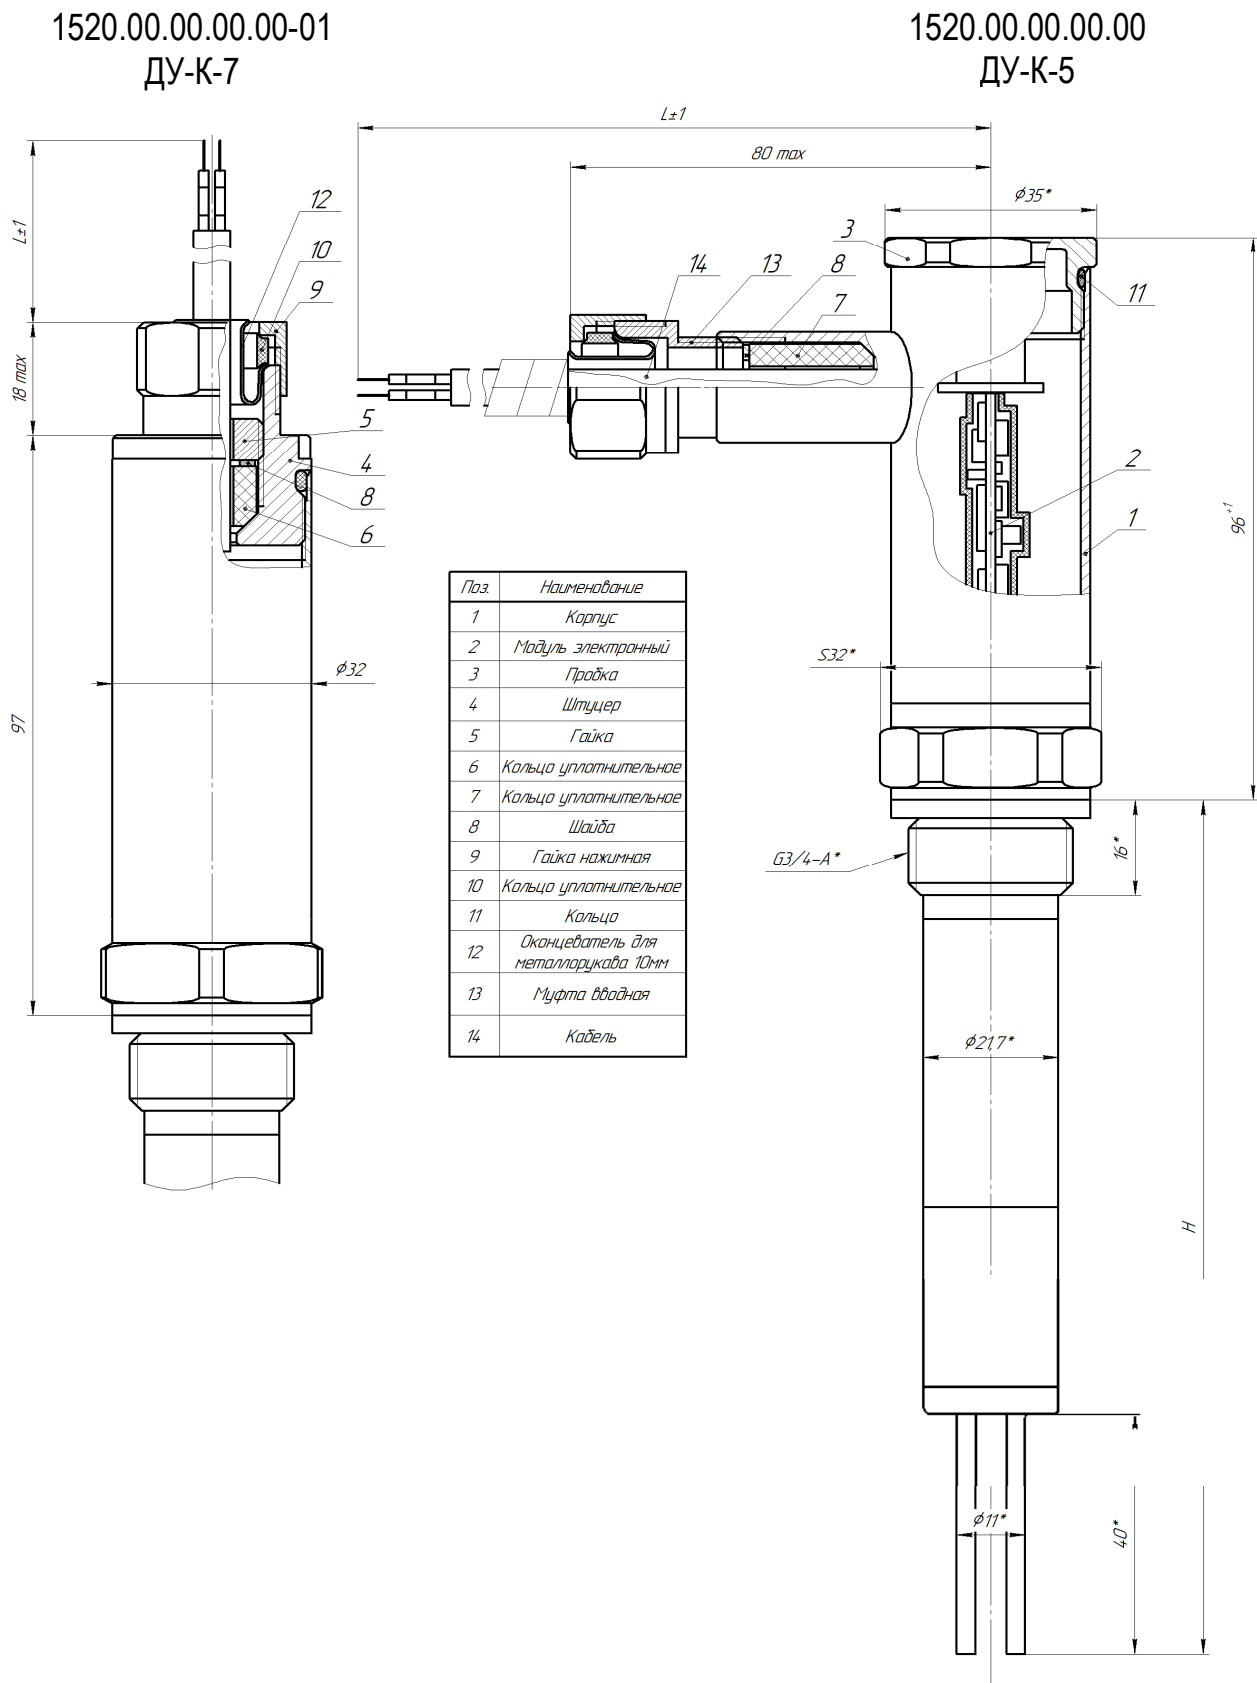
ДУ-К. Устройство, габаритные и присоединительные размеры
